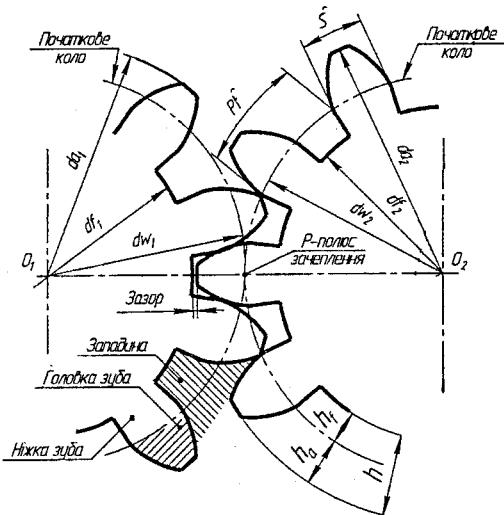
Зачеплення (gearing) пари циліндрических коліс
